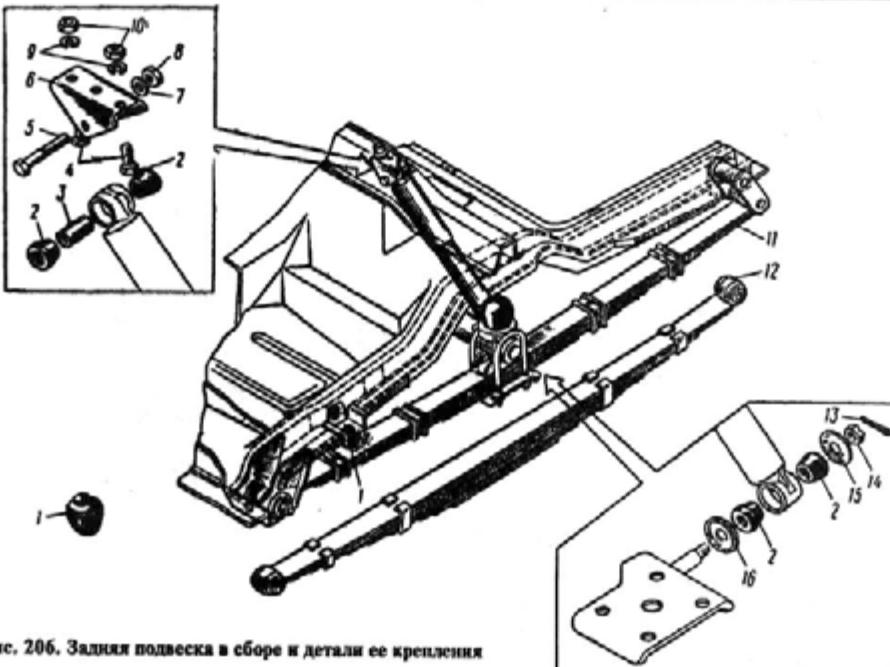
Задняя подвеска в сборе и детали ее крепления
